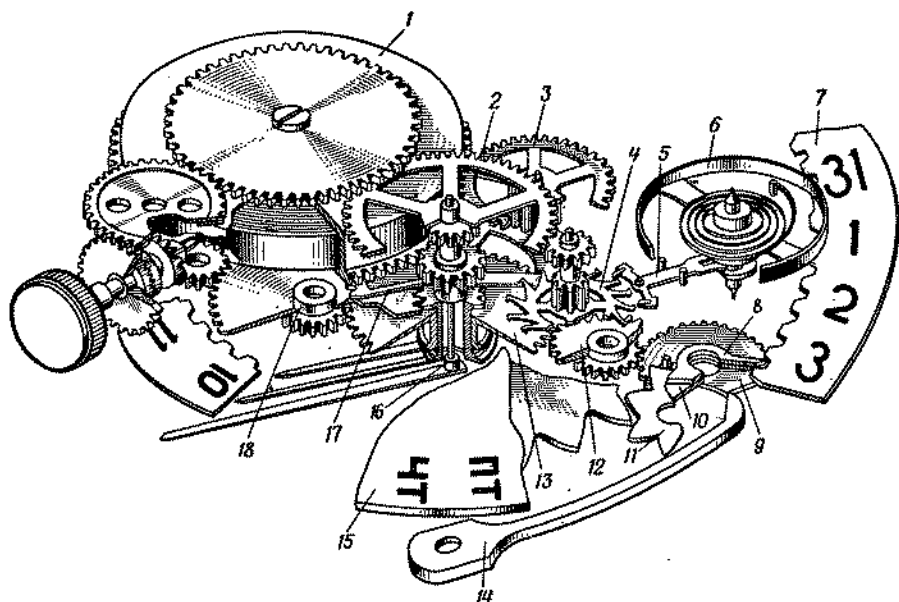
Кинематическая схема часов «Ракета» 2628:
